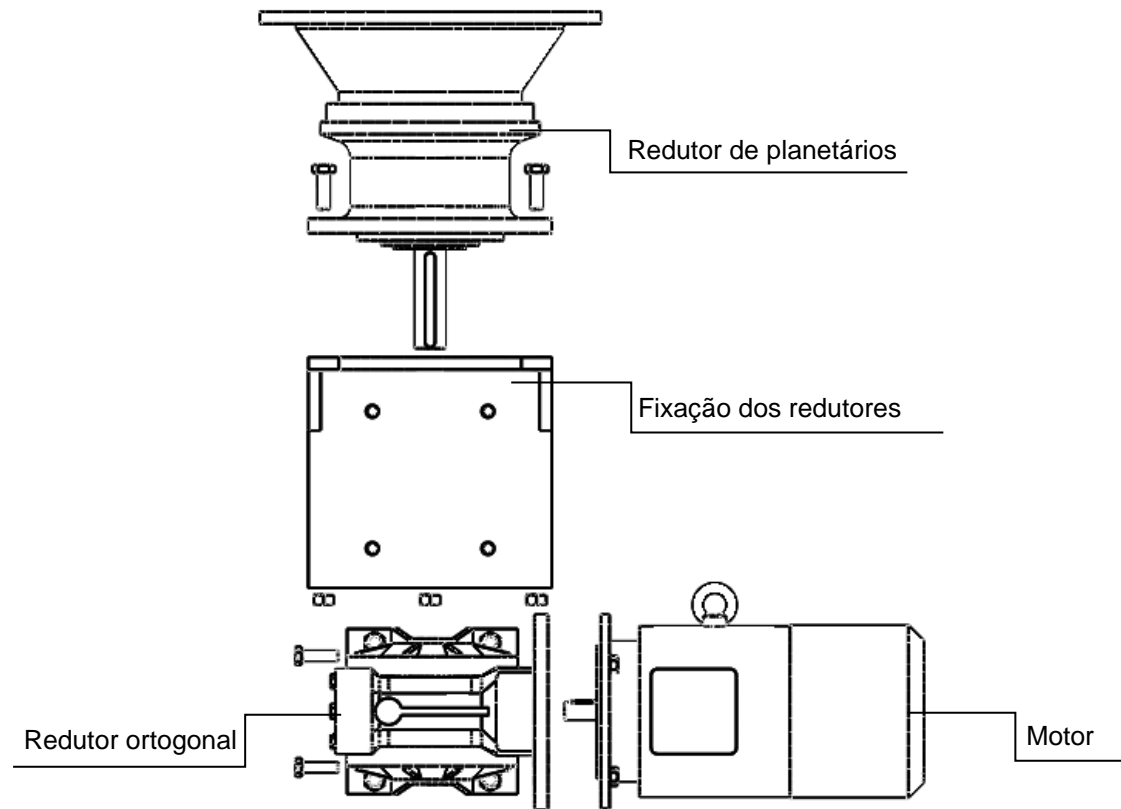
Vista explodida do conjunto motor - redutores.
